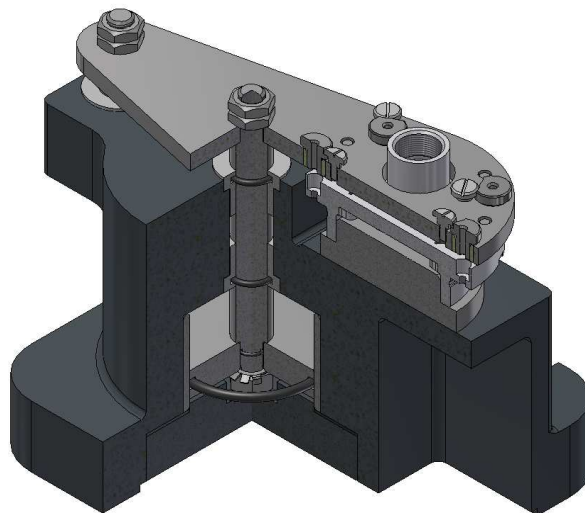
3D модель пневматического кондуктора с закрепленной заготовкой
